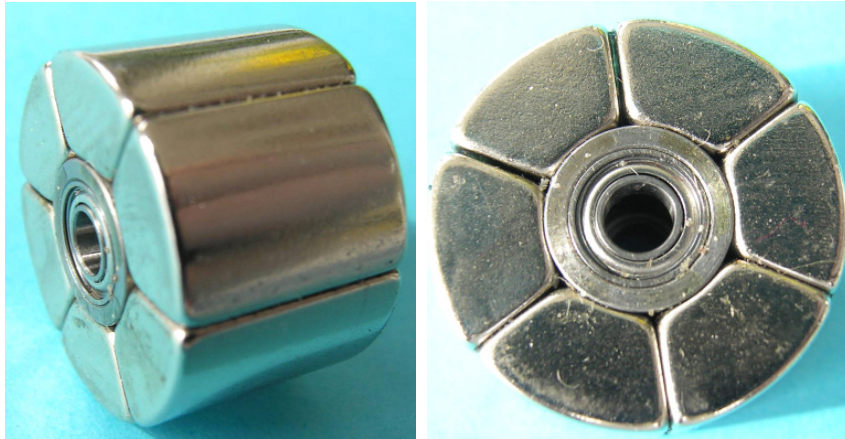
Polrad mit zwei Kugellagern: 11 mm lang, 15 g schwer, 6 NeFe-Magnetsegmente
